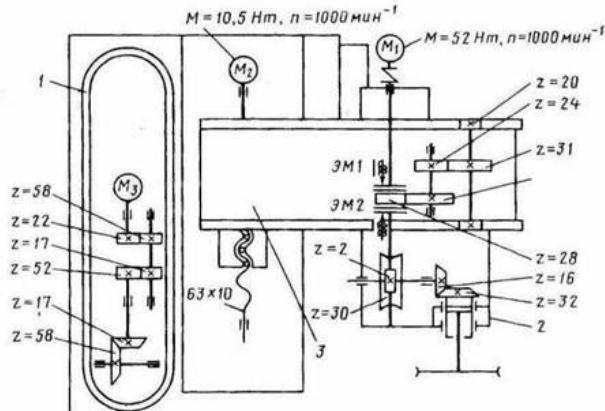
Кинематическая схема МАСИ расточного станка
